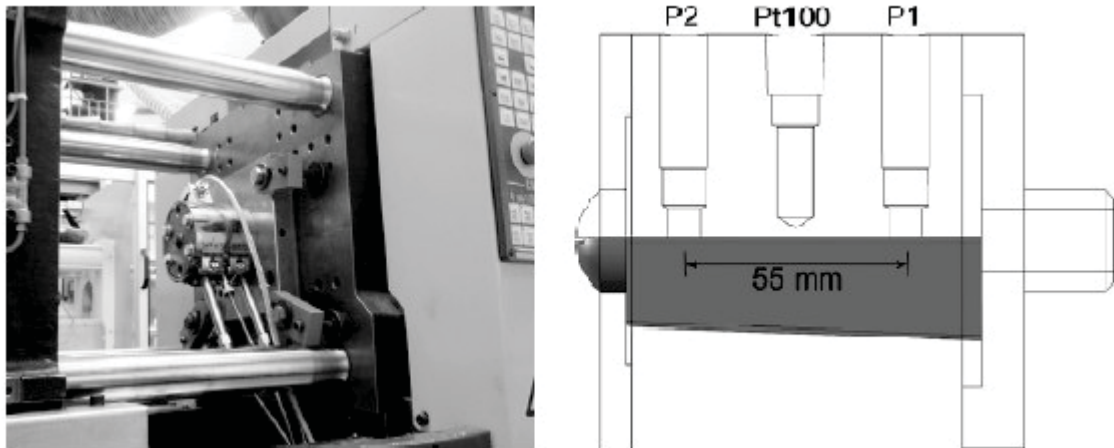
Spritzgießmaschinenrheometer montiert auf der Werkzeugplatte (links) Schlitzdüsenwechseleinsätze (rechts) [2].
